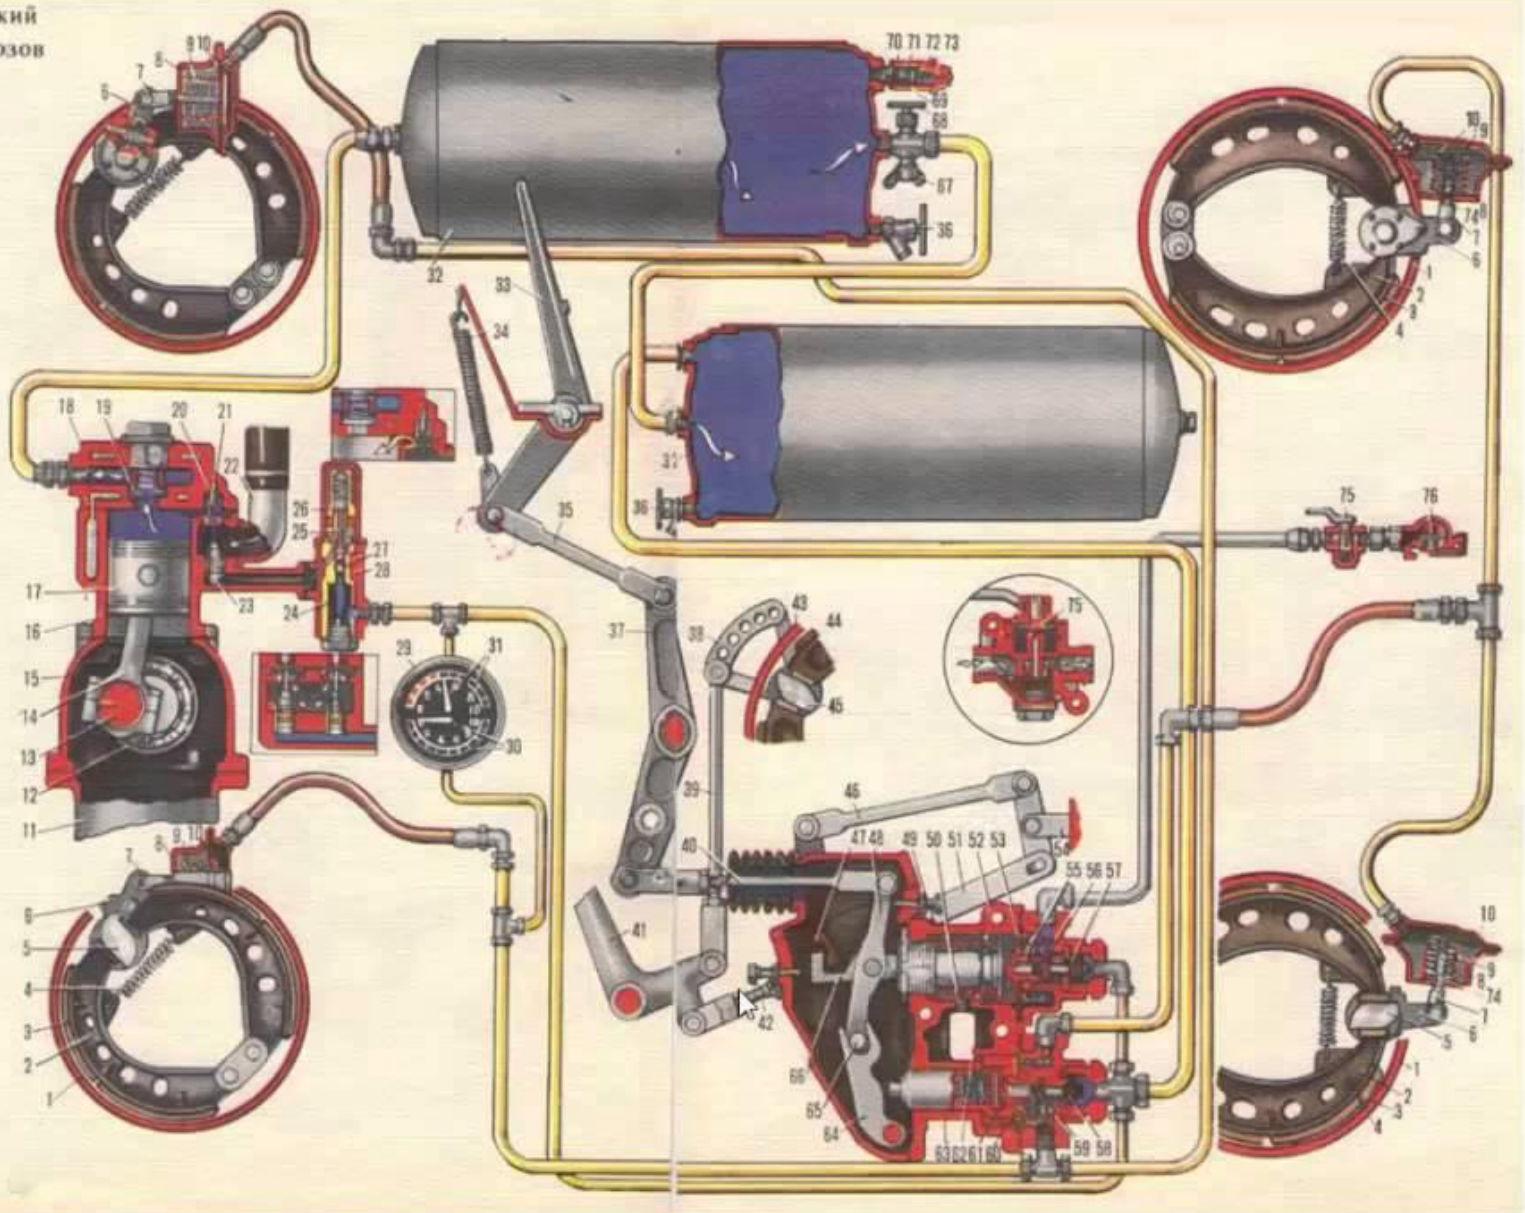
Схема пневматического привода гальм ЗІЛ-130
